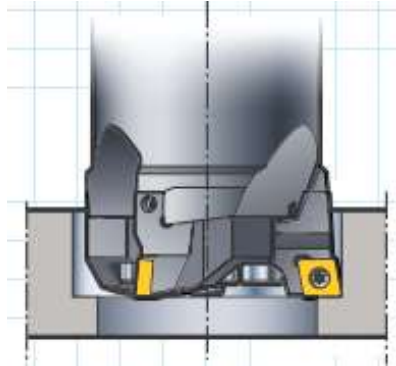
Інструмент для чорнової обробки з декількома ріжучими кромками
